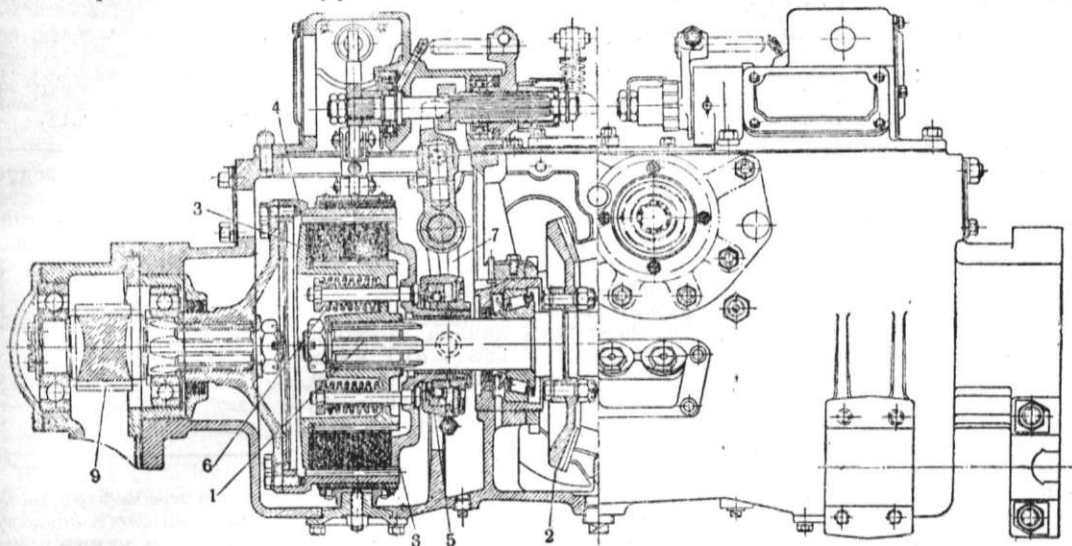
Муфты управления (бортовые фрикционы) трактора СХТЗ-НАТИ: 1—вал муфт управления; 2—коническая шестерня; 3—ведущий барабан; 4—ведомый барабан; 5—отводка; 6—пружина муфт управления; 7—рычаг; 8—нажимной диск; 9—ведущая шестерня конечной передачи.
